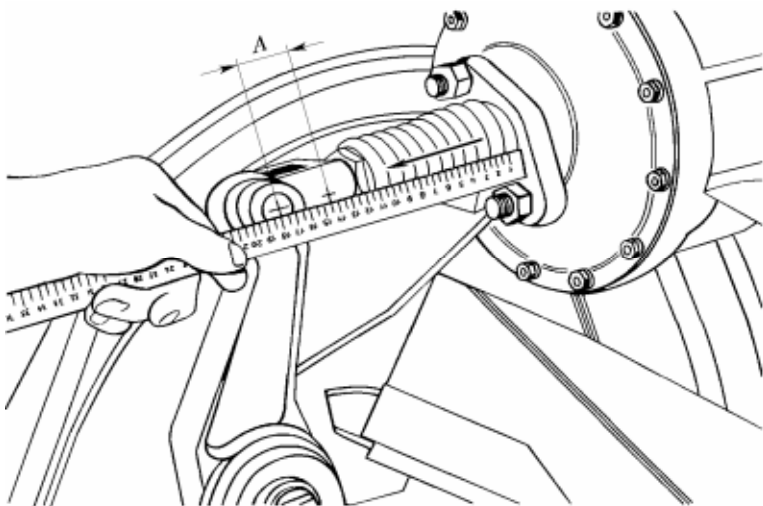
Регулировка хода штока цилиндра тормозного механизма рабочей тормозной системы
